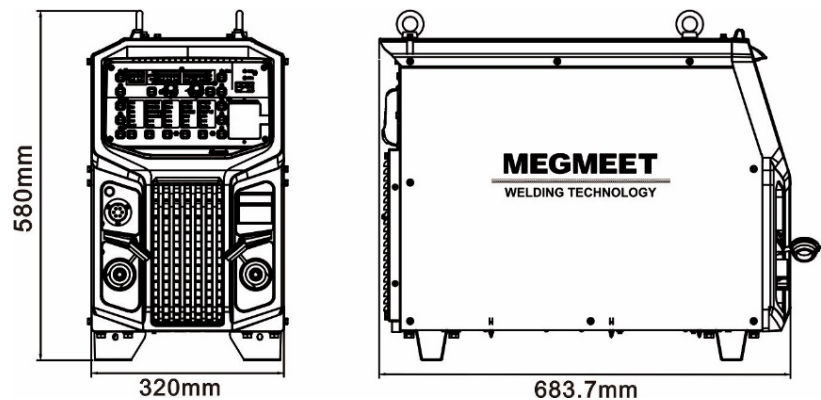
焊接电源外观及尺寸（单位：mm）
